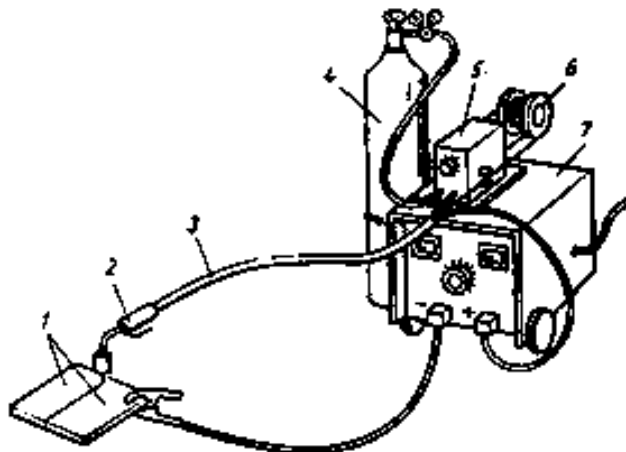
Пост для полуавтоматической сварки в среде CO_2 :
